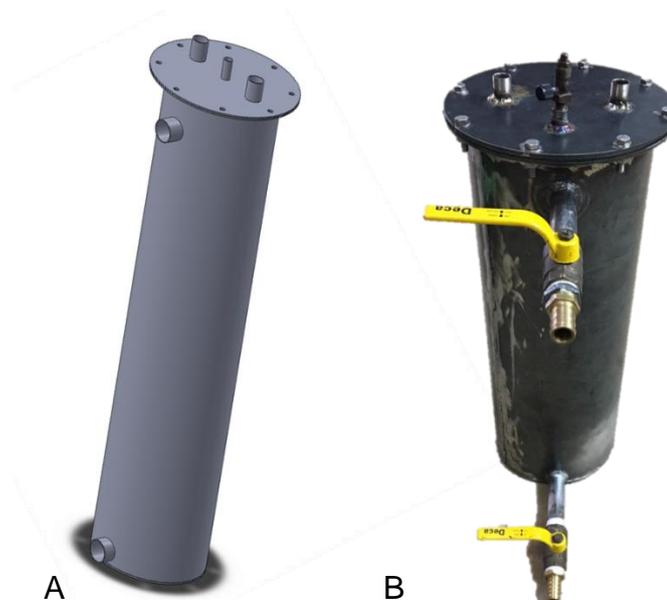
A: Modelagem chiller utilizando software paramétrico. B: Chiller confeccionado e soldado estanque. Fonte: fonte própria
